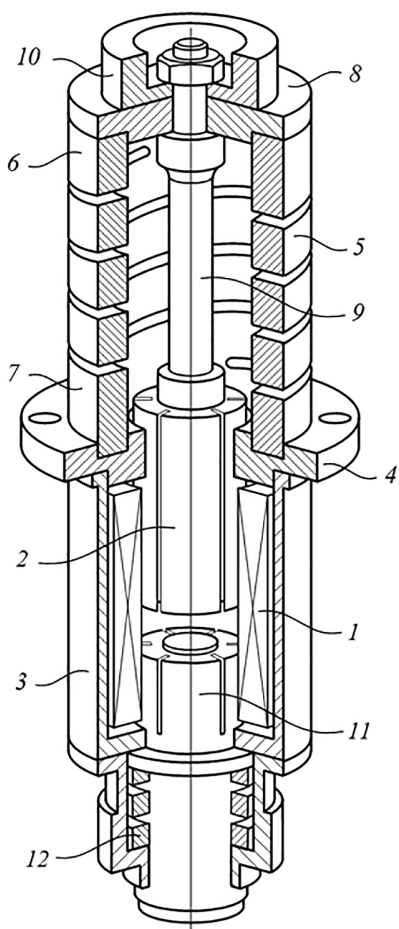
Однокатушечный электромагнитный вибровозбудитель: 1 – катушка возбуждения; 2 – якорь в виде сердечника; 3 – статор; 4 – корпус; 5 – пружина растяжения-сжатия; 6, 7 – витки-фланцы пружины; 8 – опорная плита; 9 – соединительный шток; 10 – регулировочный груз; 11 – подвижный сердечник; 12 – пружина сжатия
